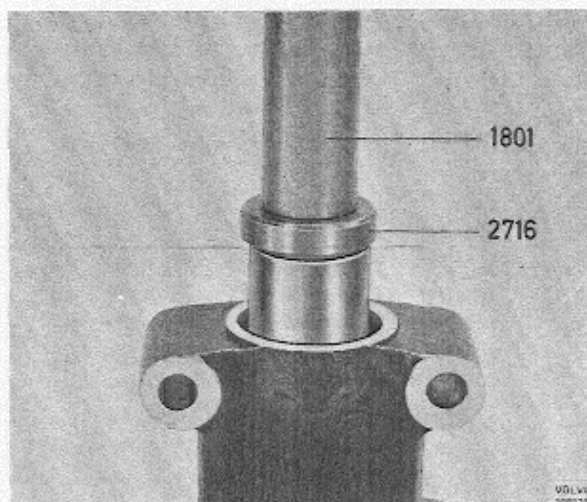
Einpressen der Buchsen, Lenkrollenwelle
